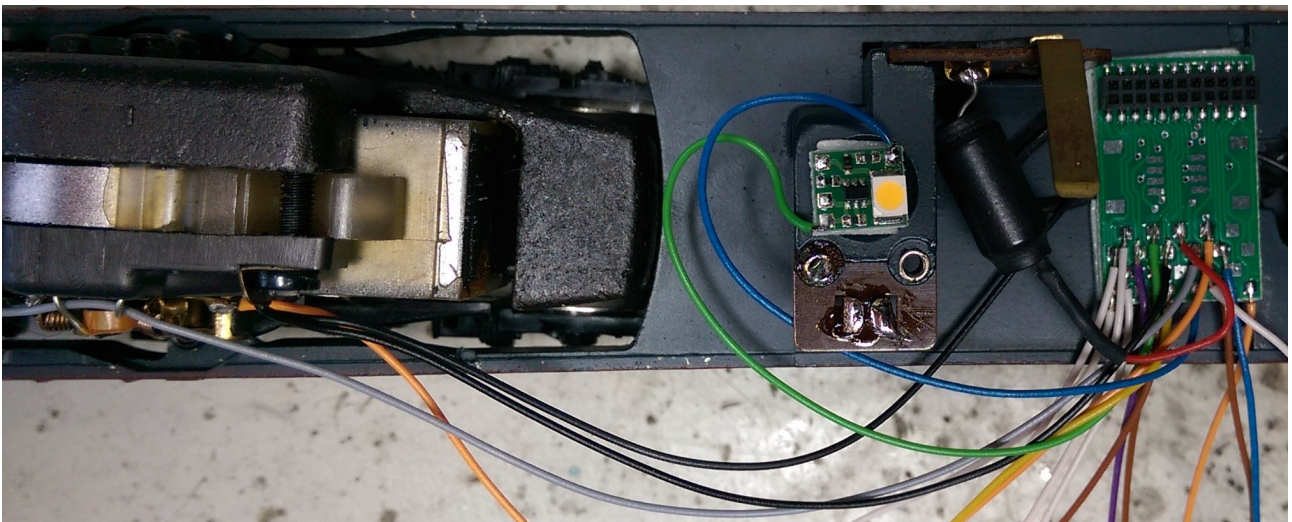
Maschinenraum-Beleuchtung und Motor sind an den Adapter angeschlossen.
